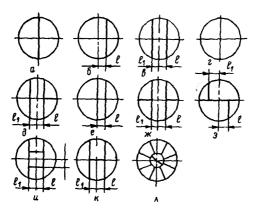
Расположение сварных швов заготовок выпуклых дииц
